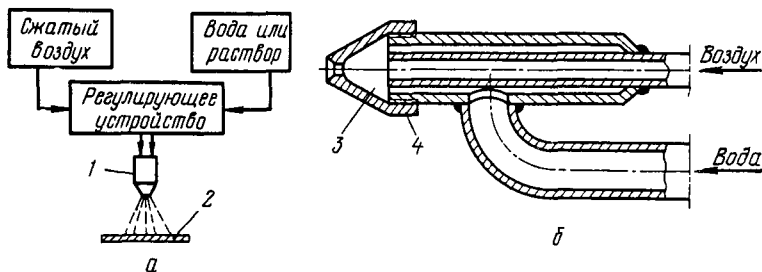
Установка для мойки тары и оборудования воздушными форсунками: а — схема установки; б — водовоздушная форсунка: 1 — форсунка; 2 — обрабатываемая поверхность; 3 — камера смешения; 4 — сопло
